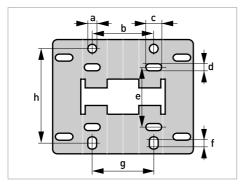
Dimensions de la plaque de montage pour boîtier mural
